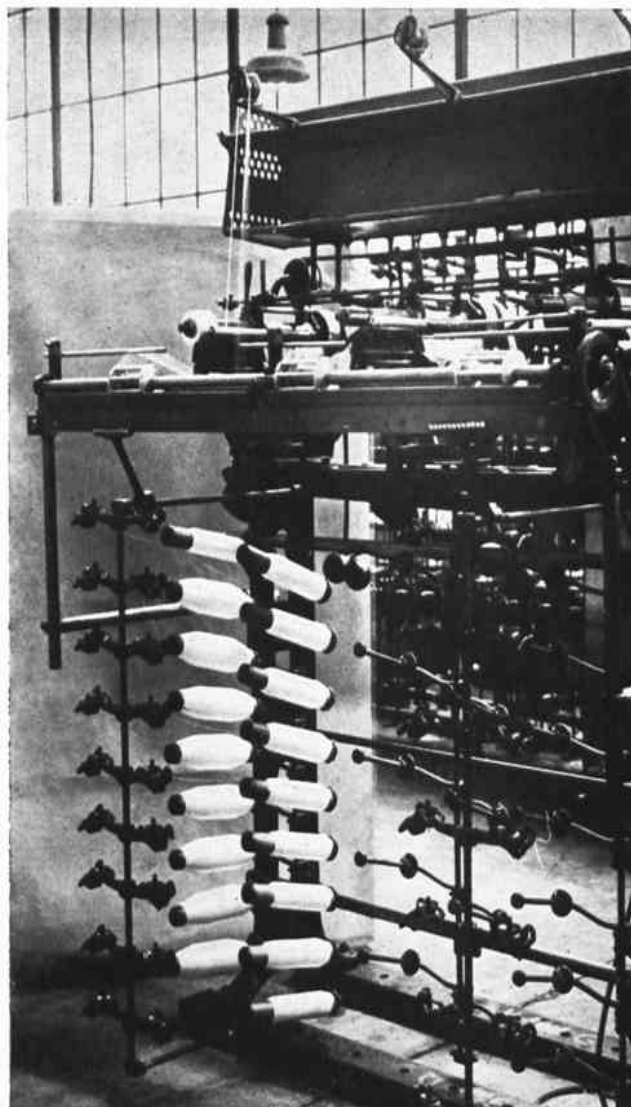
Bobinoir à assembler avec dispositif de surensimage.
